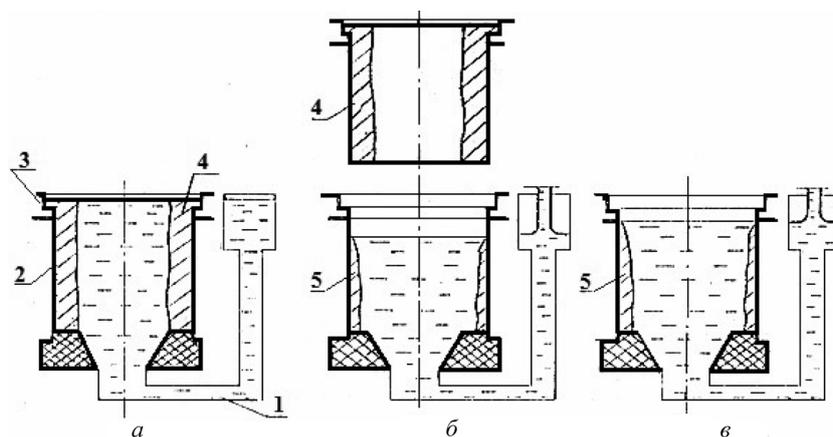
Этапы формирования отливок (а, б, в) и принципиальная схема литья полых заготовок намораживанием без стержня: 1 – литниковая система; 2 – стационарный кристаллизатор; 3 – подвижный кристаллизатор; 4 – сформированная отливка; 5 – формирующаяся отливка
